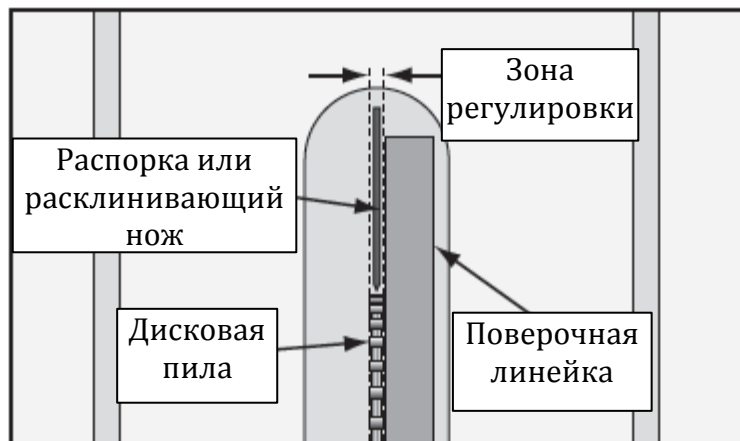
Зона регулировки распорки или расклинивающего ножа
